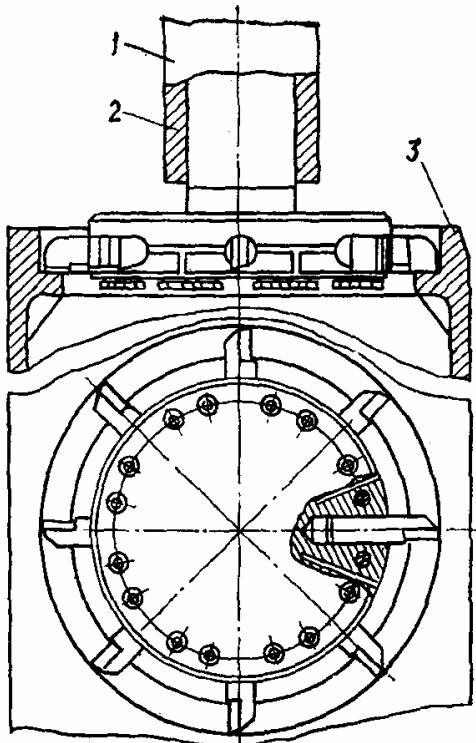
Багаторізцева оправка для обробки виточок блока під бурти гільз циліндрів:
